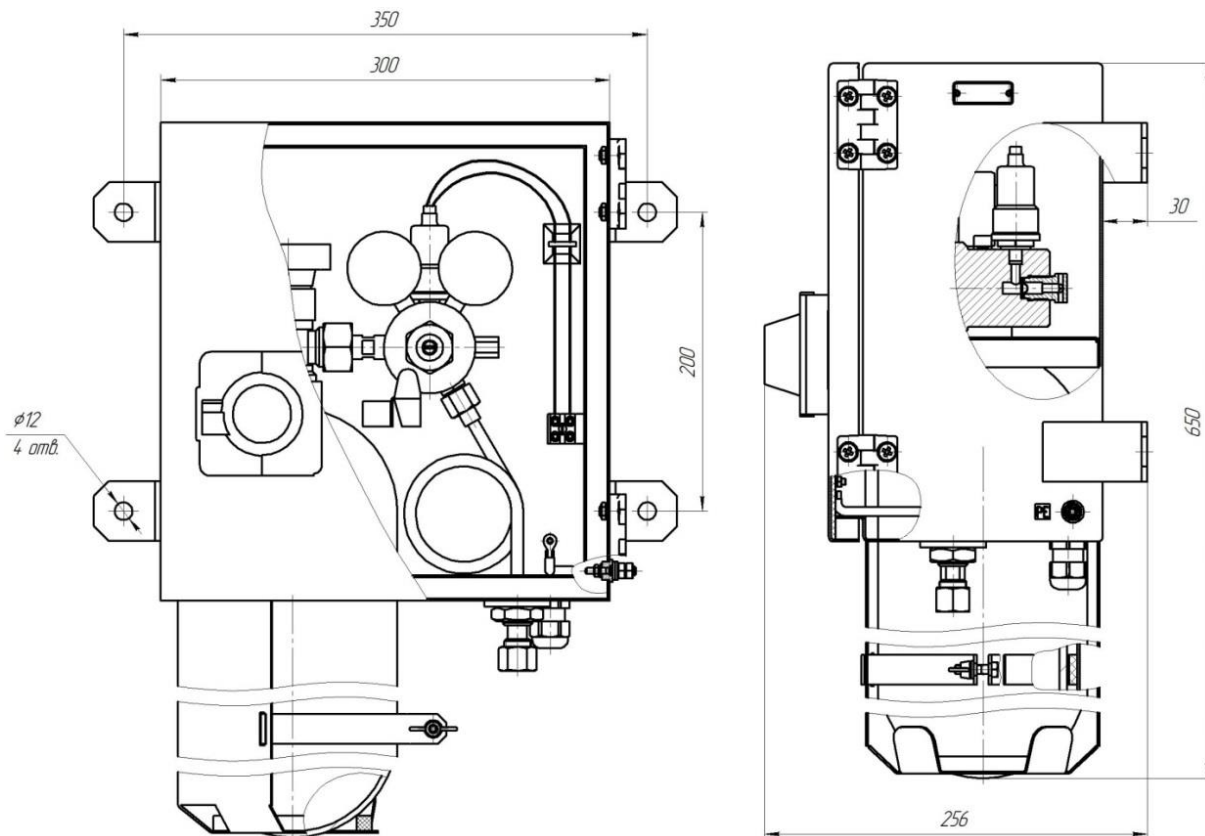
Габаритные размеры ресивера PCB-5
